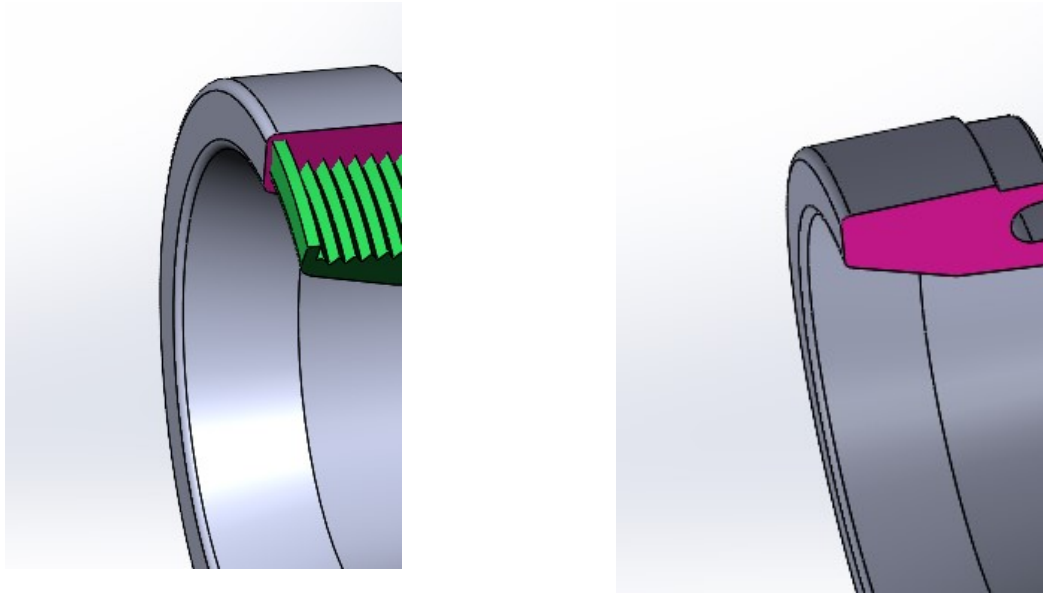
3Д моделі заготовки (відливка в кокіль)
